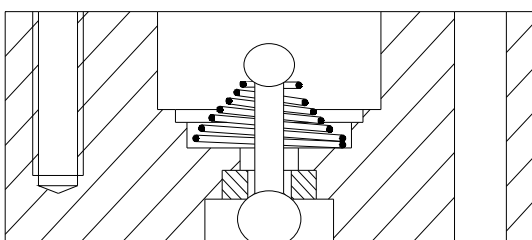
"ASSEMBLAGE DETAILS (38), (39) ET (41)"
